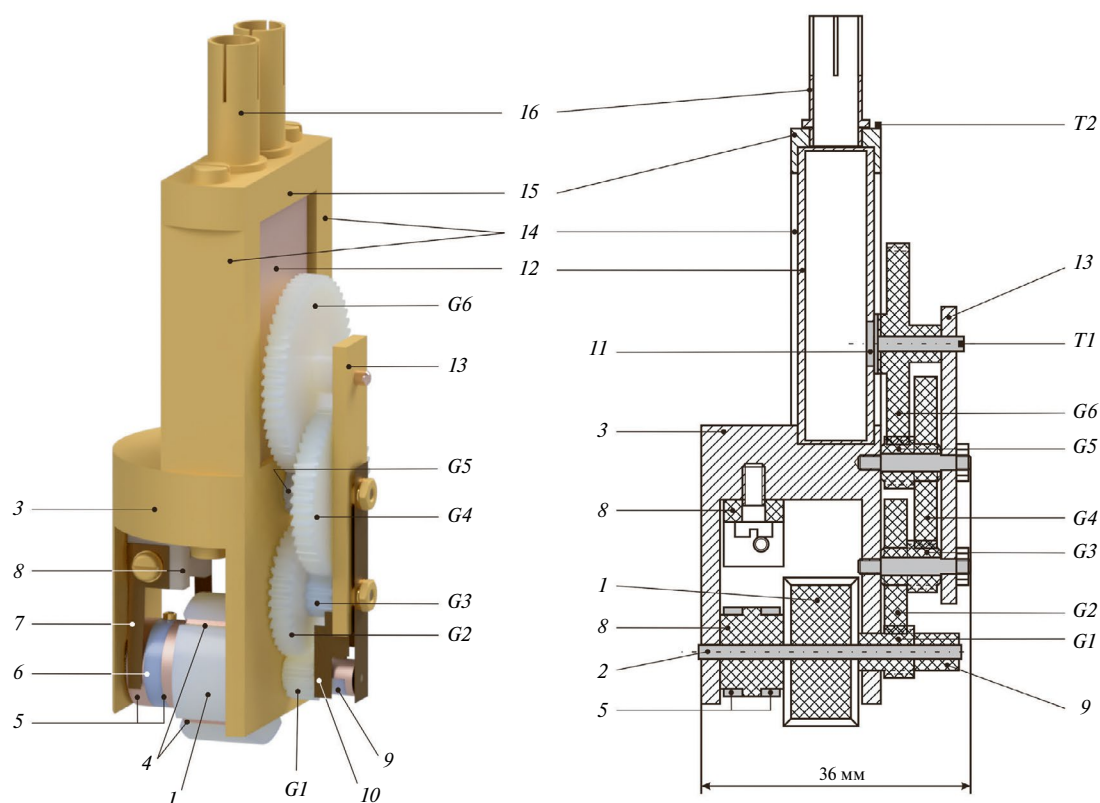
Конструкция вращательного механизма на СВЧ резонаторе: слева – внешний вид, справа – разрез. Детали механизма: 1 – барабан, 2 – ось, 3 – корпус, 4 – обмотки, 5 – медные кольца, 6 – втулка, 7 – бронзовые лепестки, 8 – держатель лепестков; 9, 10 – втулка и скользящие контакты датчика поворота, 11 – ось с монтажной площадкой для образца, 12 – резонатор, 13 – прижимная планка, 14 – крепежные стойки, 15 – верхний фланец, 16 – цанги волноводов, G1–G6 – шестерни, T1, T2 – термометры RuO₂. Штрихпунктирные линии – поворотные оси механизма.
